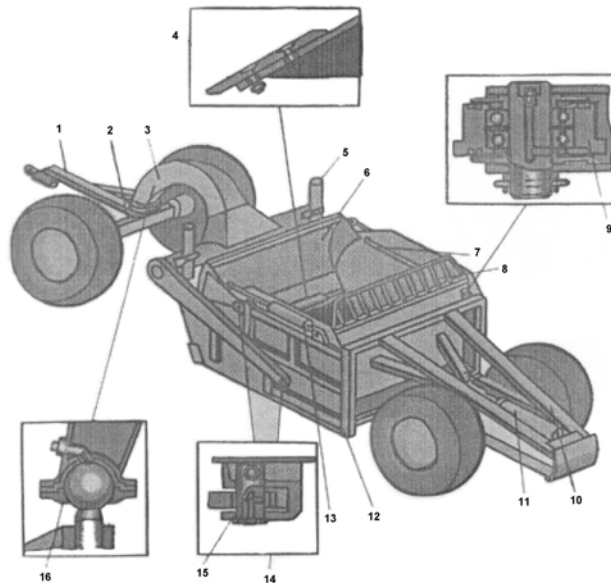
Скреперное оборудование:1-дышло;2-ось;3-тяговая рама;4- нож;5- гидроцилиндр подъема ковша;6-заслонка;7- направляющая;8- задняя стенка;9- ролик;10- Буферная рама;11- гидроцилиндр задней стенки;12-ковш;13- гидроцилиндр заслонки;14- палец крепления тяговой рамы;15-палец крепления заслонки;16-шаровое соединение.
